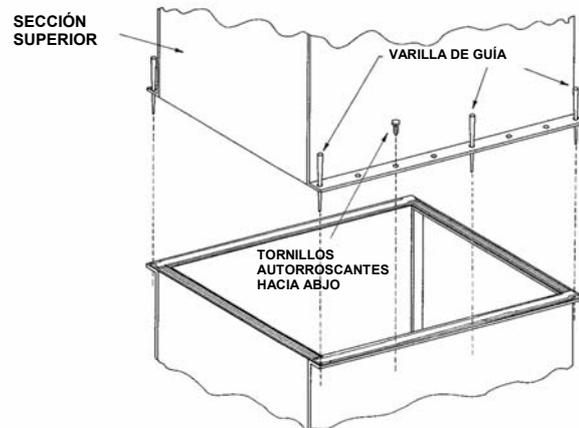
Emparejamiento de la Sección Superior sobre la Sección de Bandeja
